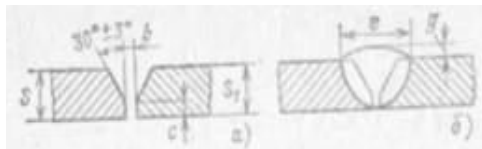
Сварной шов с размерами кромок:
